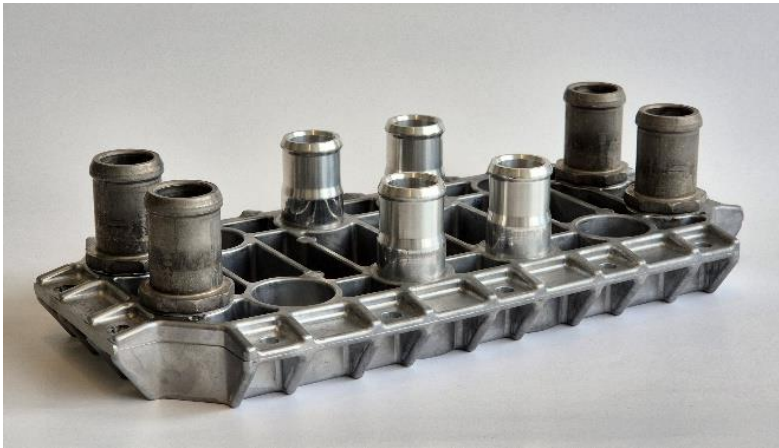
Endplatte mit reibgeschweißten (außen) und eingegossenen Elementen (innen)
